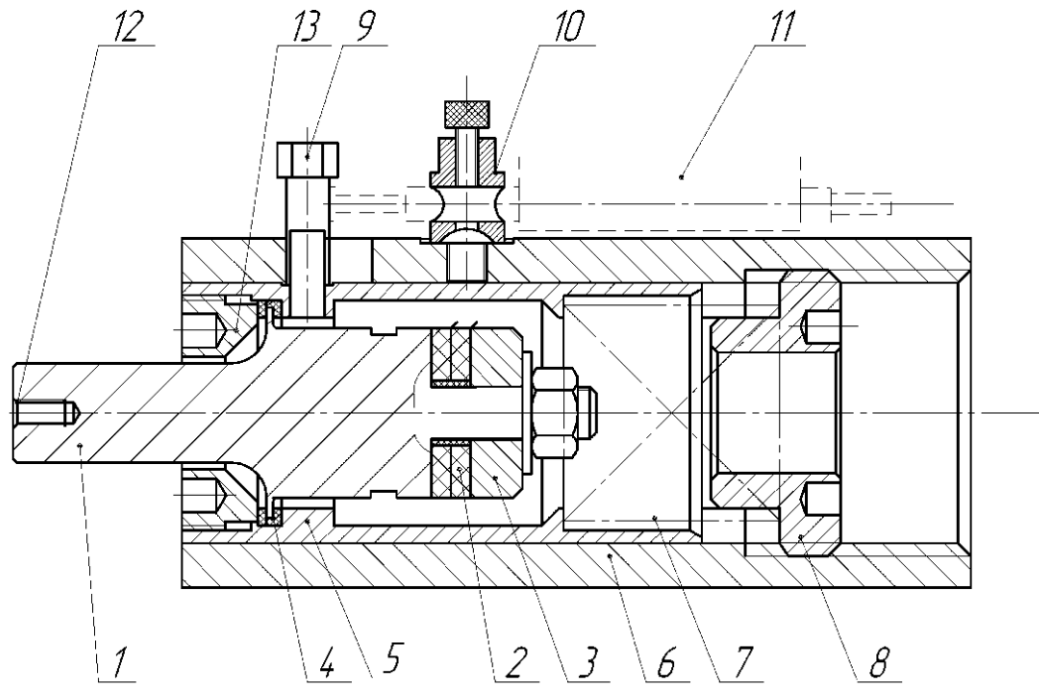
Загальний вид пристрою для ультразвукового вигладжування
